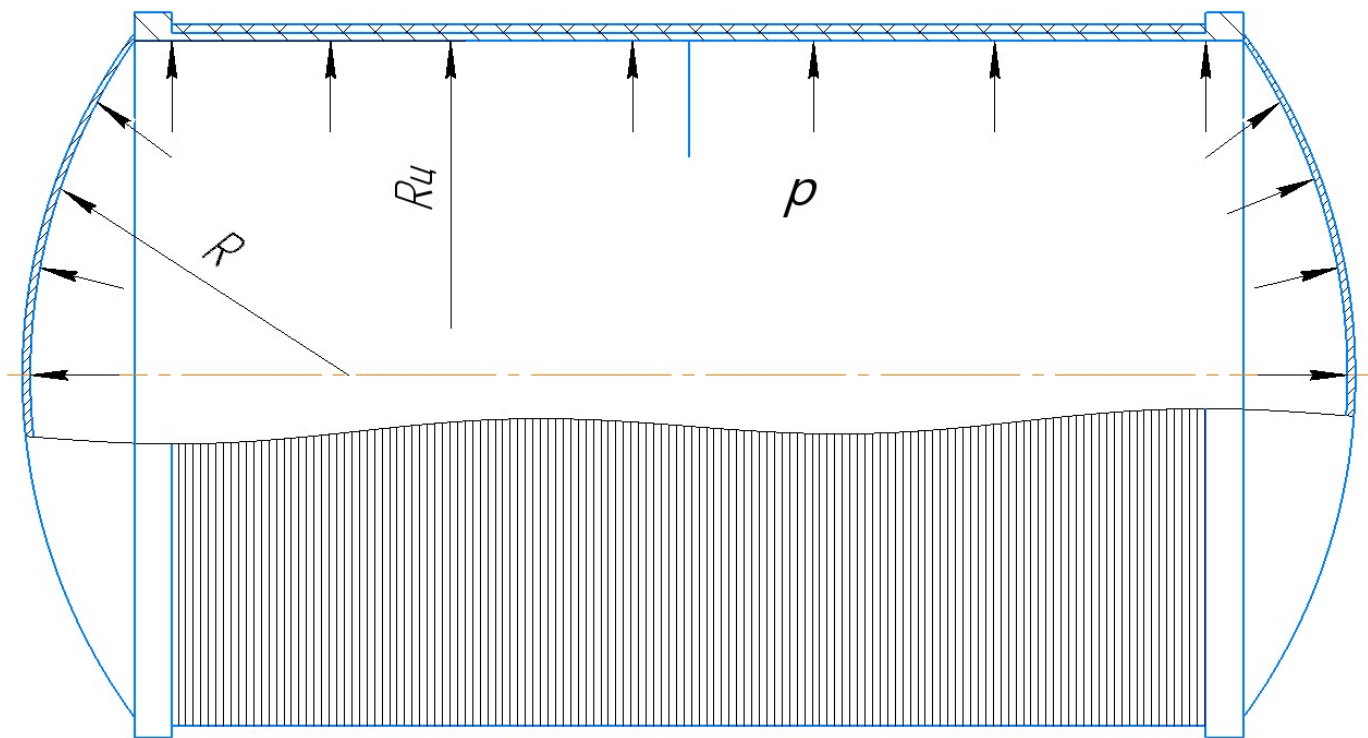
Схематическое изображение сечения металлокомпозитного бака с металлическими днищами
